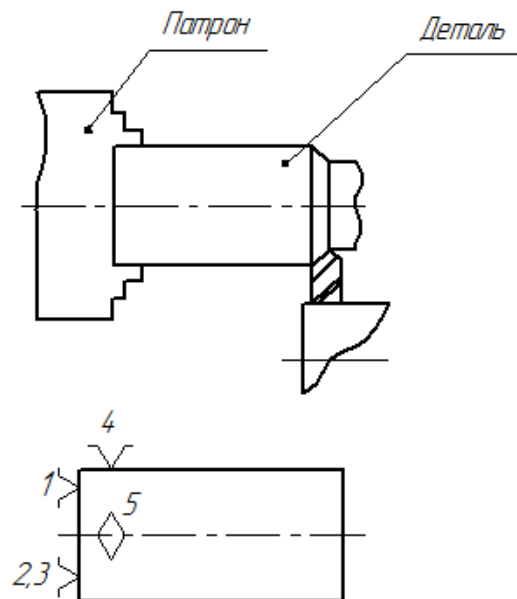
Установка й схема базування заготовок у трьохкулачковому патроні, що самоцентрується
